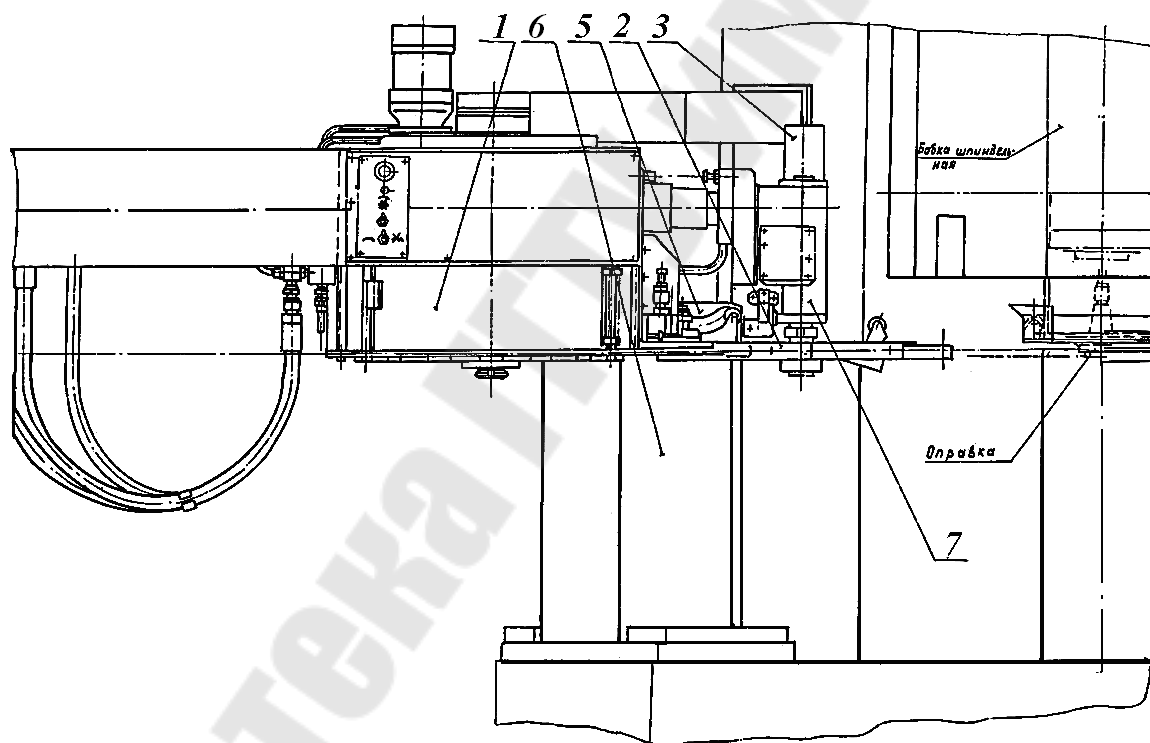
Эскиз устройства автоматической смены инструментов
